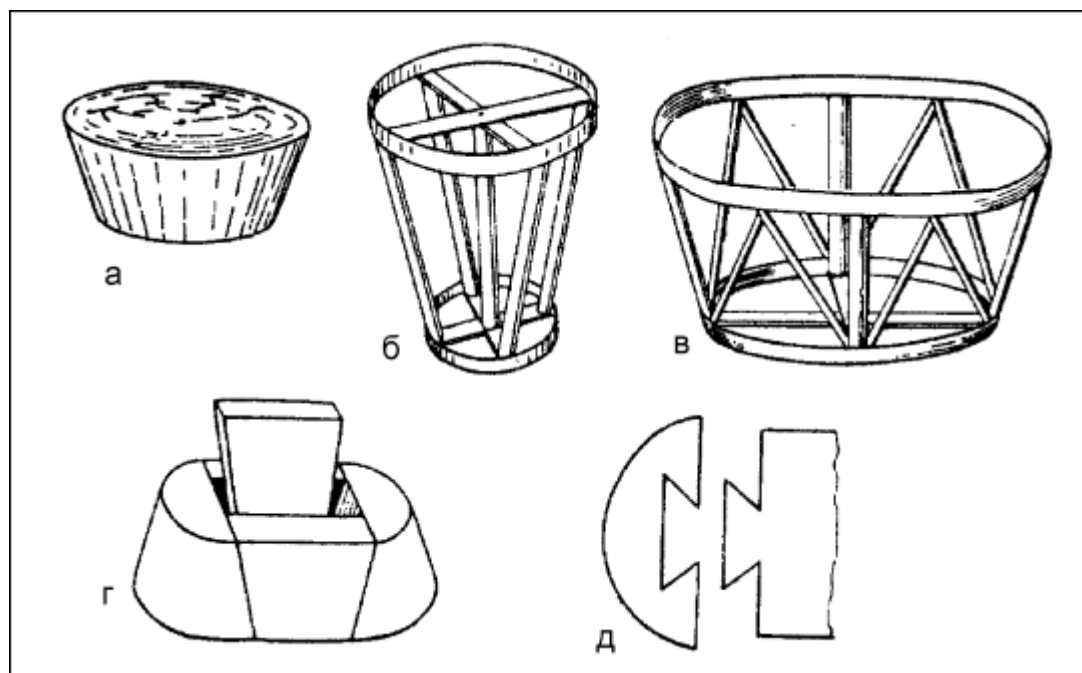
Шаблоны: а – неразборный болваночный; б, в – неразборные каркасные; г, д – соответственно разборный (общий вид) и схема соединения его деталей с устройством шипового соединения «ласточкин хвост»
